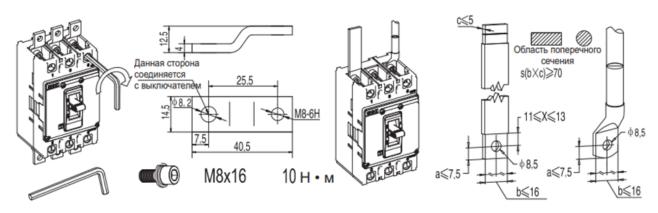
NXM(S)-160 размеры соединительной пластины и кабелей
